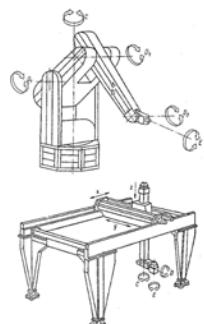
Зварювальний робот фірми «Німак» (Німеччина)
